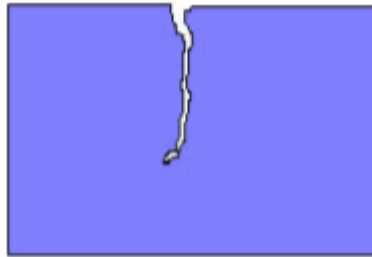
Inspección de tintes penetrantes; zona de inspección.
